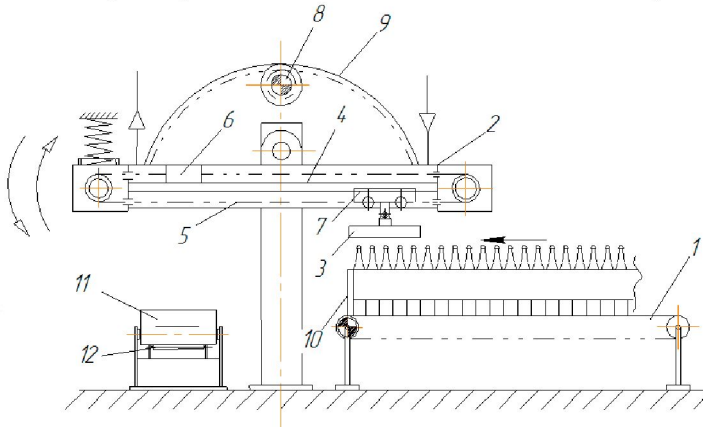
Схема укладальної машини з коливальним рухом траверси: 1- стіл – накопичувач; 2- траверса; 3- захоплювальна головка; 4 – пневмоциліндр; 5- гнучкий елемент; 6- поршень циліндра; 7 – каретка; 8- шестерня; 9 – зубчасте колесо; 10 – планка; 11- транспортна тара; 12 – відвідний конвеєр.
